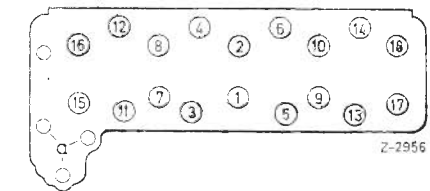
Anzugsschema für Zylinderkopfschrauben
